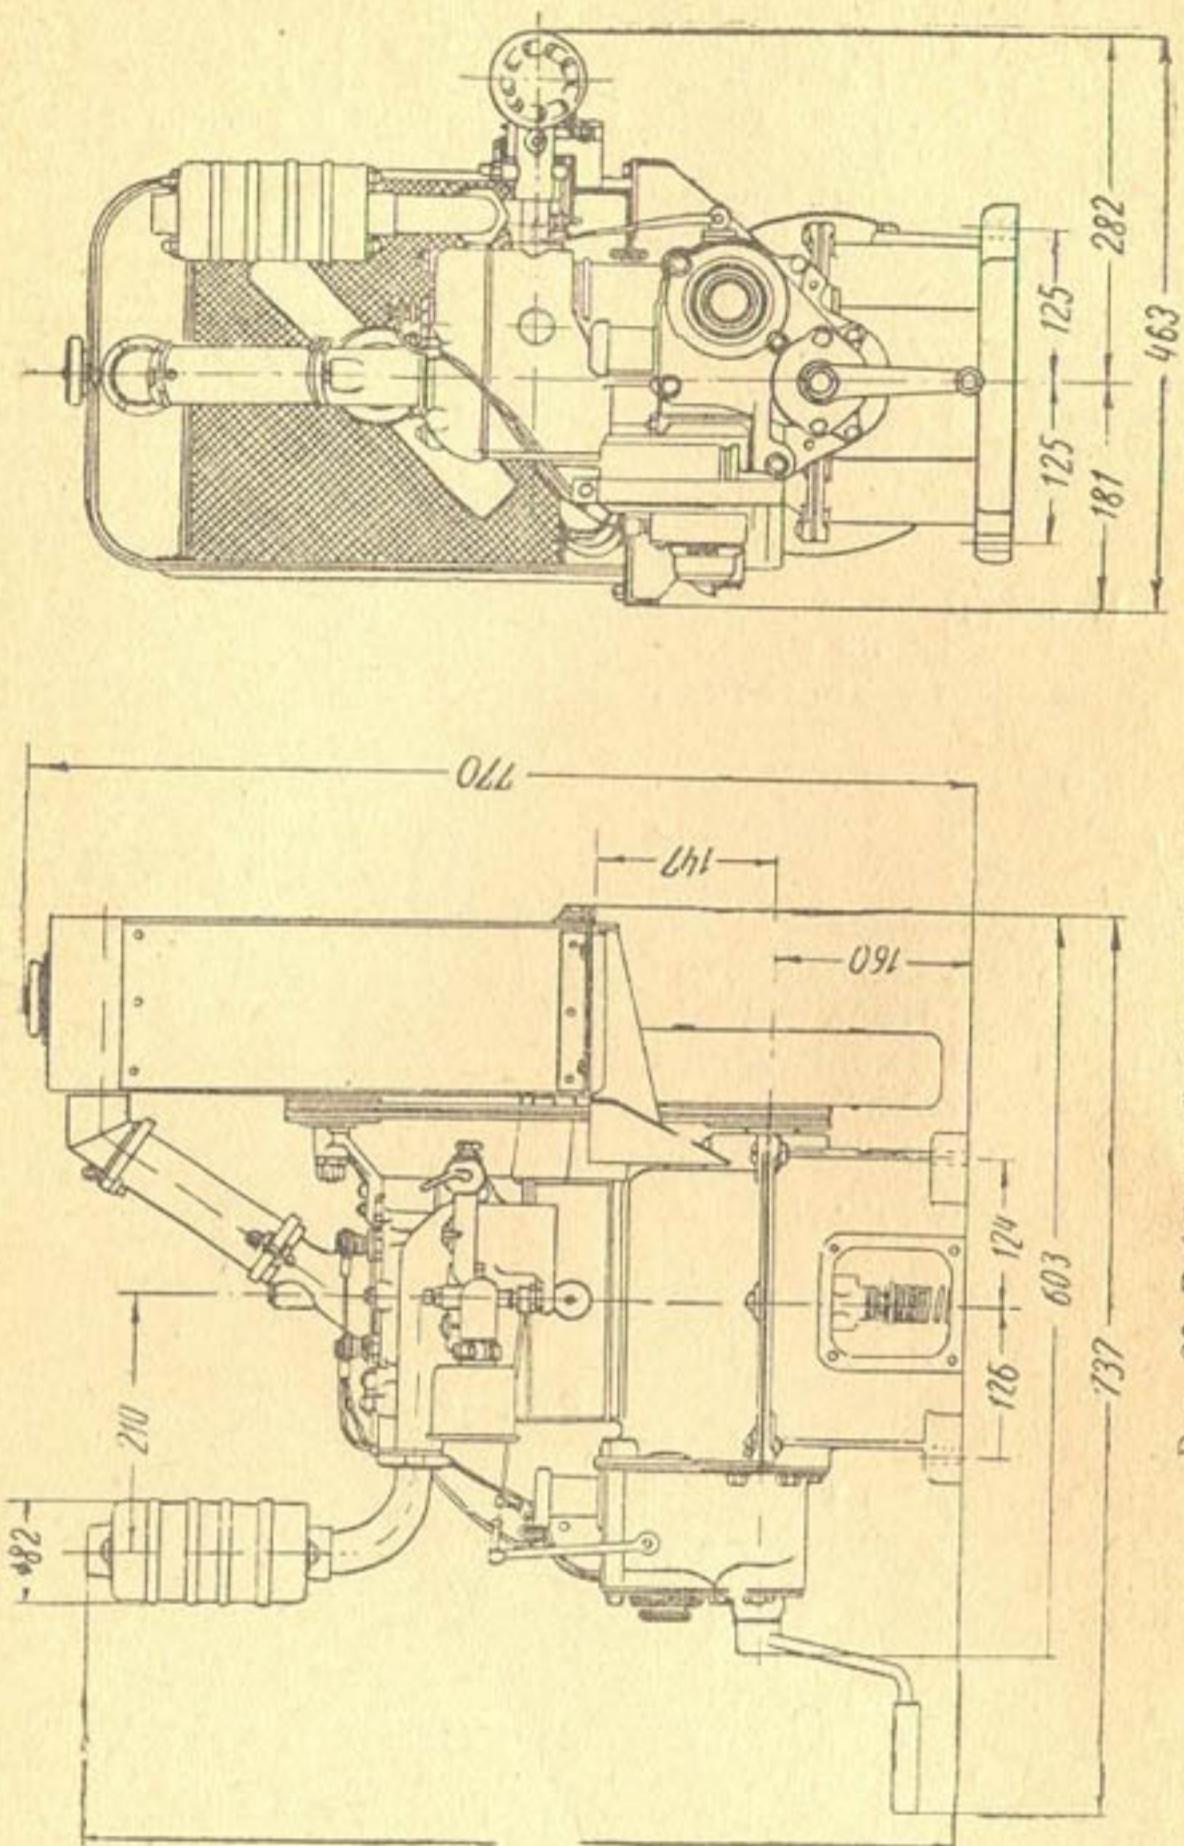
Габаритный чертеж бензинового двигателя Л-6/2.
